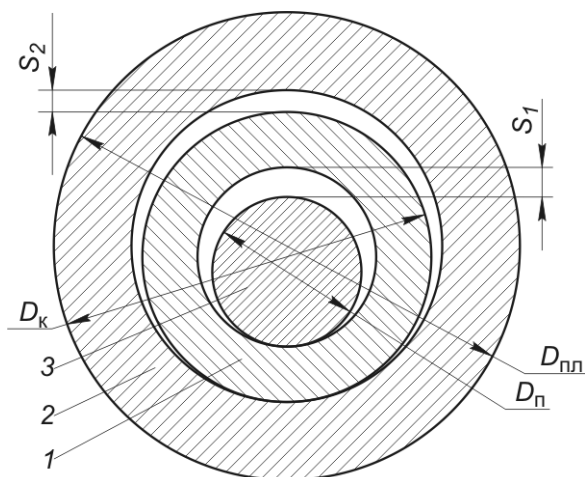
Схема зазоров в сопряжениях узла прессования: 1 – камера прессования; 2 – плита машины; 3 – прессующий поршень (плита машины условно изображена цилиндрической)
